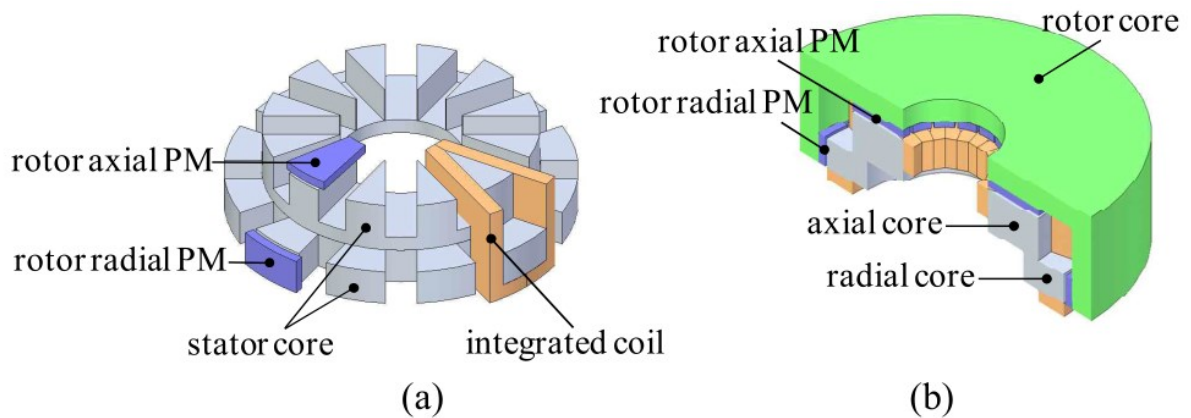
Structure de la machine hybride : (a) assemblage de la structure, (b) vue en coupe [11]
